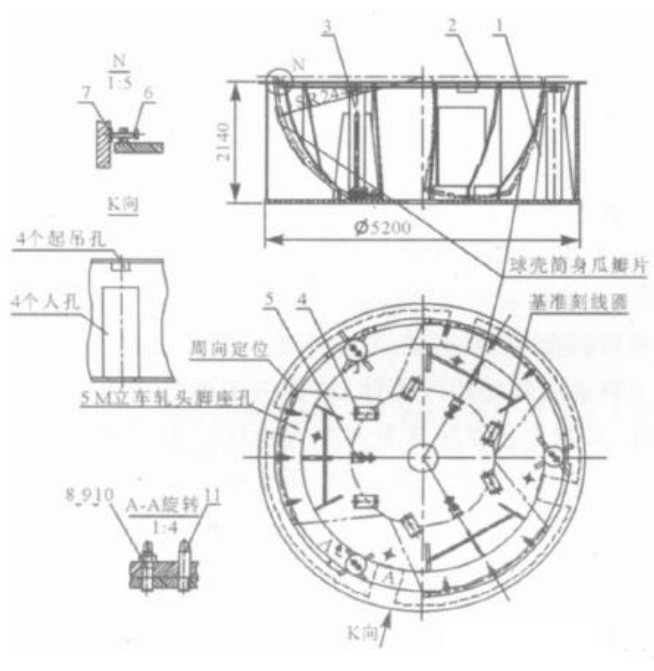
加工瓜瓣片焊接坡口的夹具
